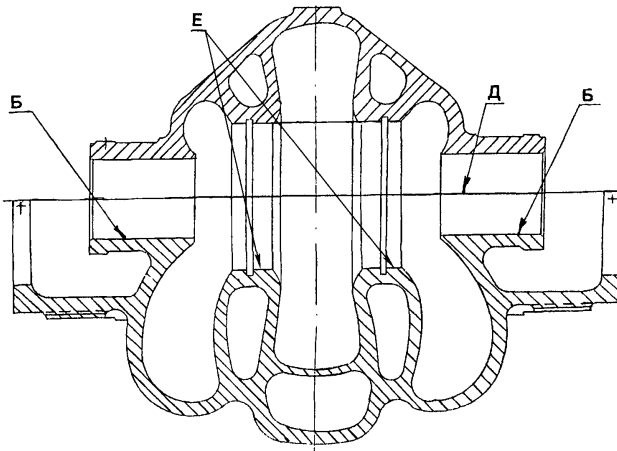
Корпус, крышка насоса СЭ 2500–60–11 (рисунок 10, поз.
